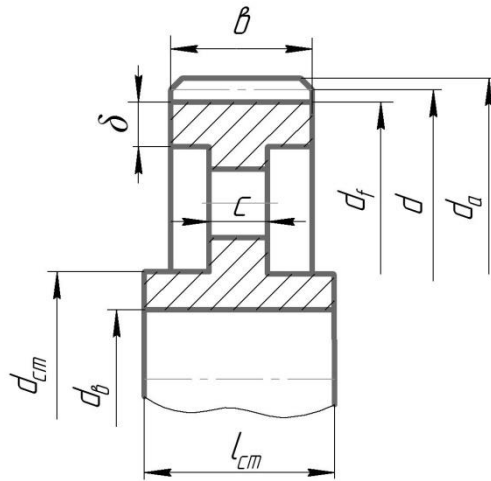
Эскизный рисунок зубчатого колеса
